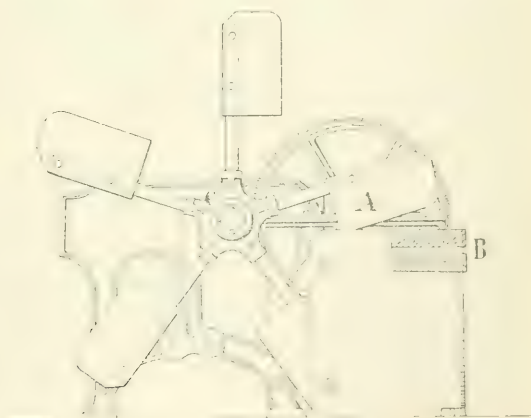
Schwingmaschine mit Schutzvorrichtung.
